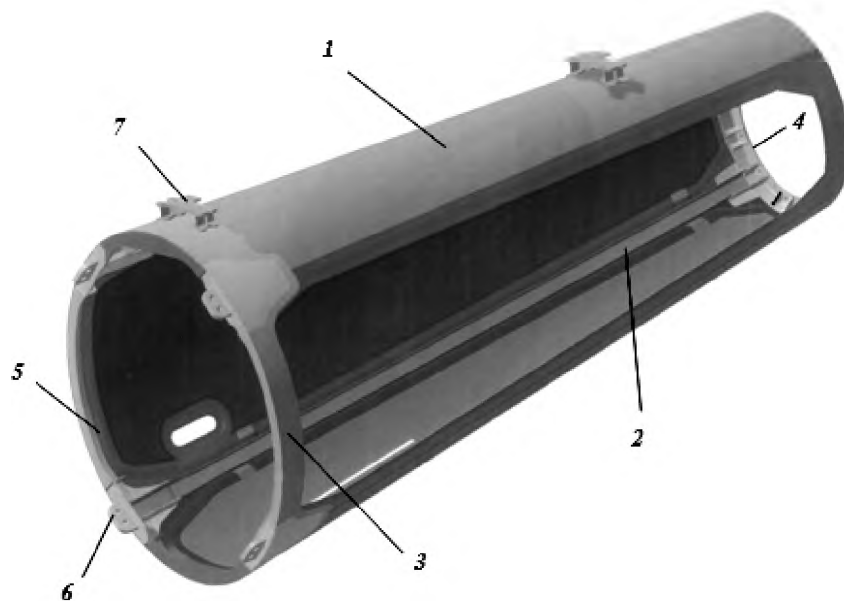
Конструкция хвостовой балки из ПКМ вертолета Ка-60
